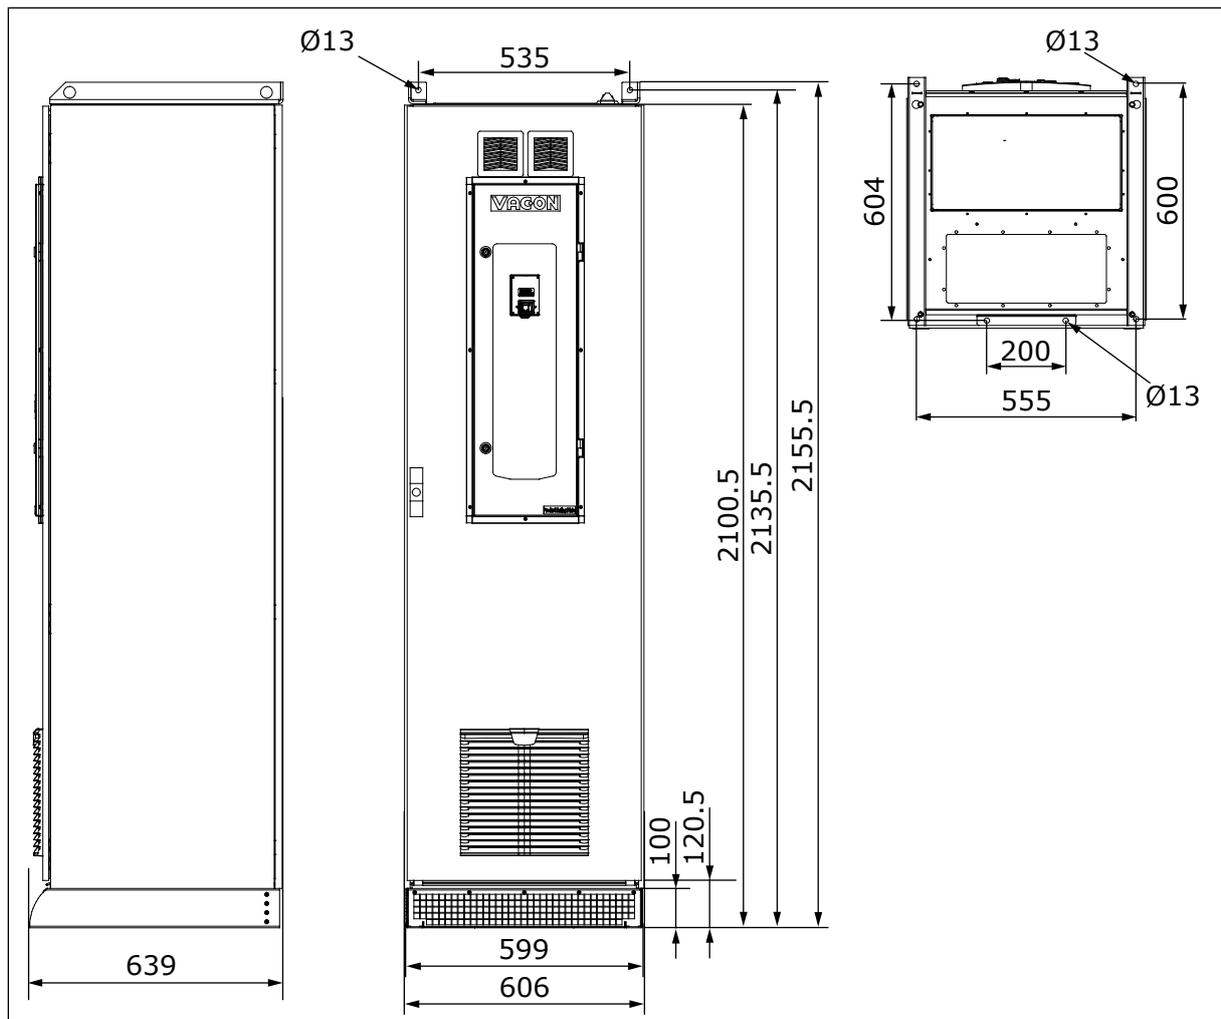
Abmessungen des Standard-Schaltschranks in mm, MR9 und MR10, IEC
